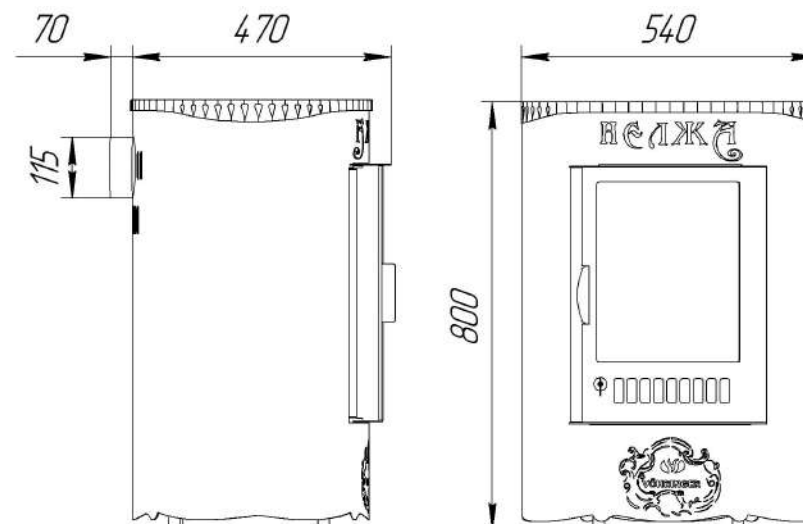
Общий вид печи с нанесенными основными размерами.
